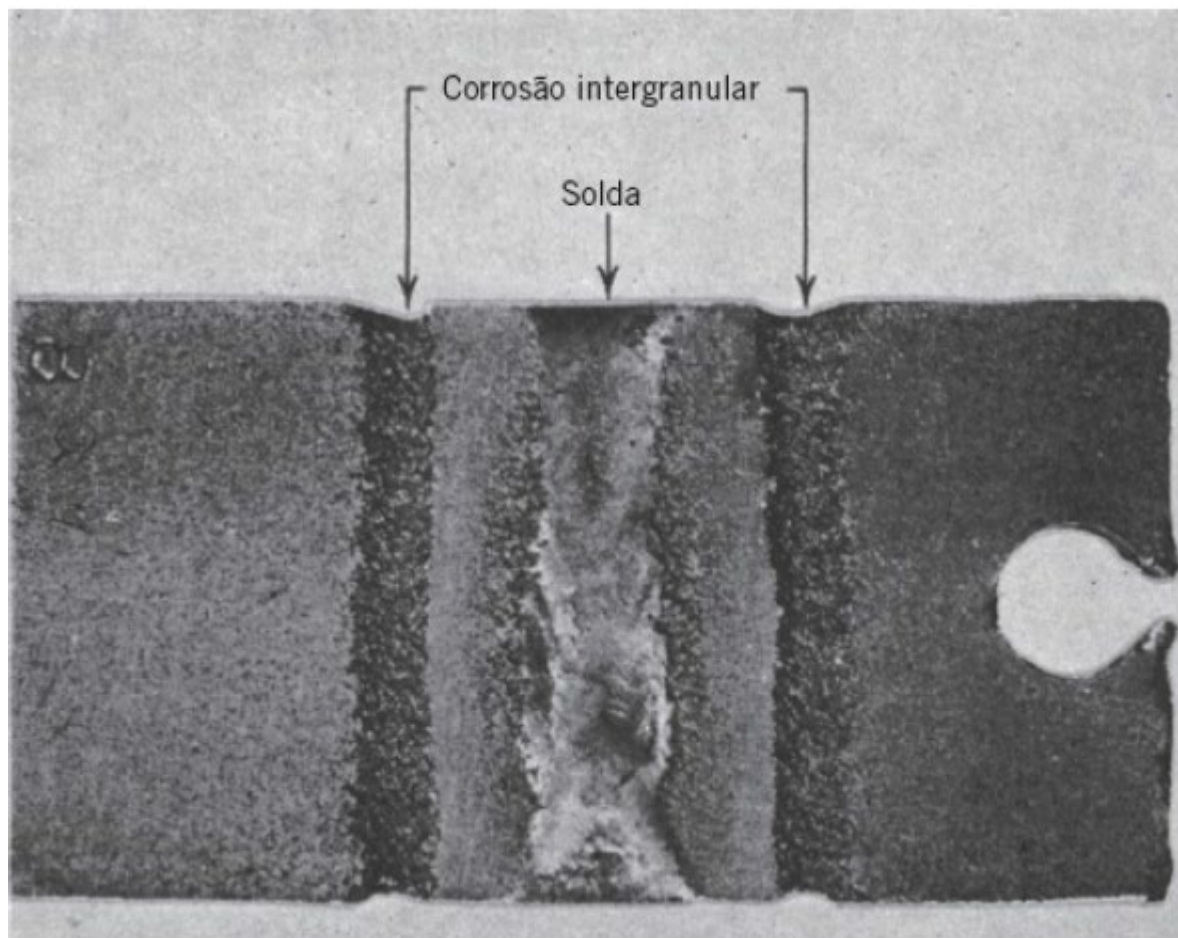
Corrosão em torno de cordão de solda [3].
